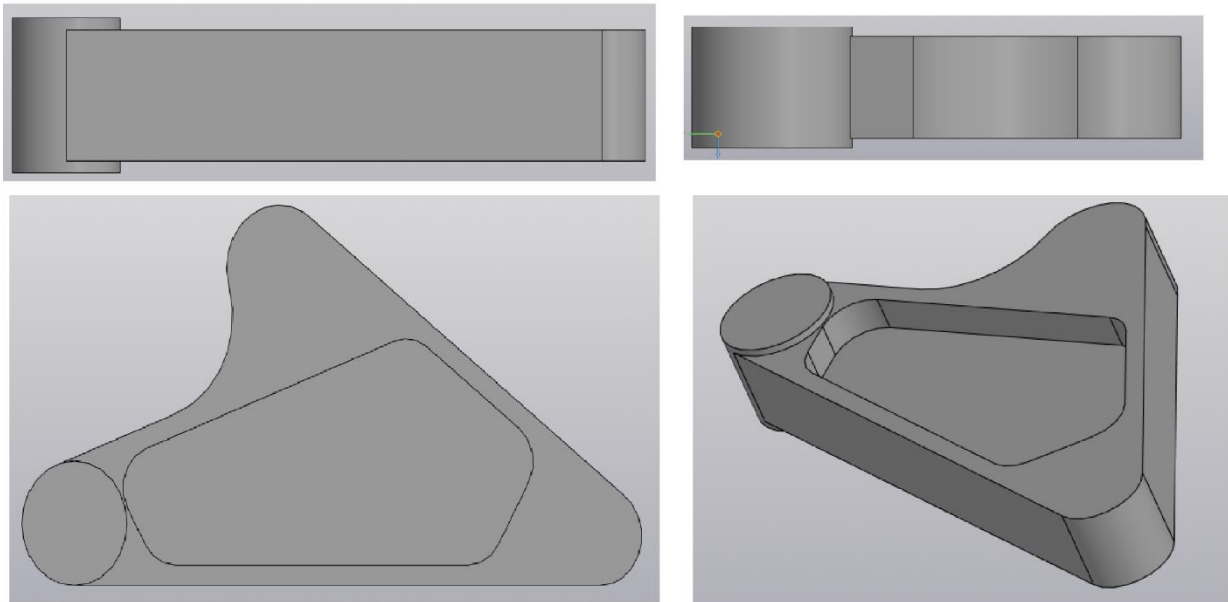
Комп'ютерна 3D-модель заготовки деталі «Качалка»
